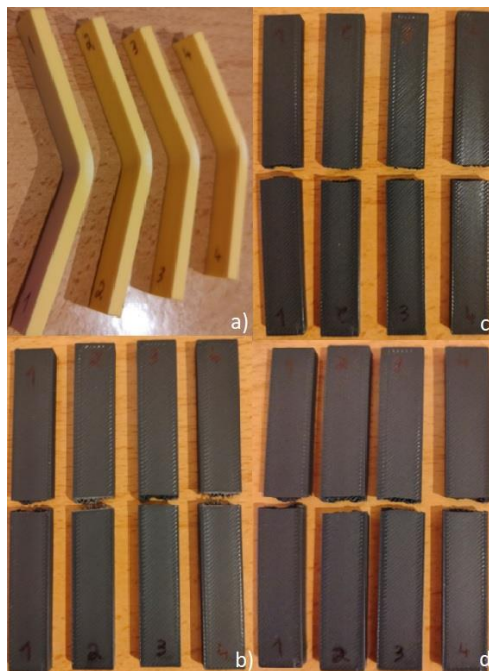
a) Provetes de PLA virgem após ensaio; b) Provetes de PLA reciclado impresso a 220°C, após ensaio; c) Provetes de PLA reciclado impresso a 237°C, após ensaio; d) Provetes de PLA reciclado impresso a 255°C, após ensaio
